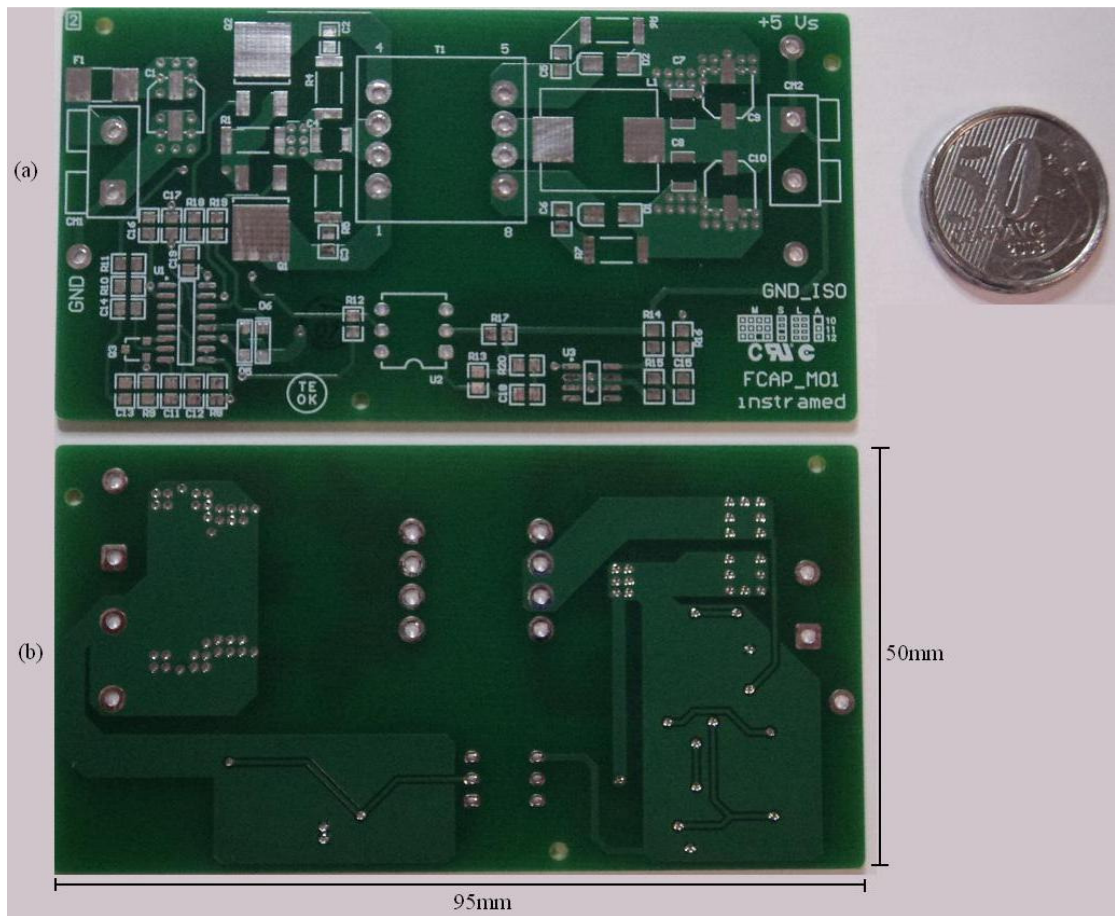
PCI completa. (a) Lado dos componentes. (b) Lado da "Solda".
